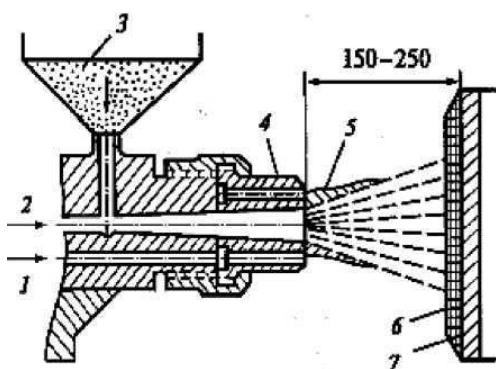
Схема напилення порошкового матеріалу: 1 - суміш кисню з горючим газом; 2 - транспортуючий газ; 3 - напилюваний порошок; 4 - сопло; 5 - факел; 6 - покриття; 7 - підкладка
